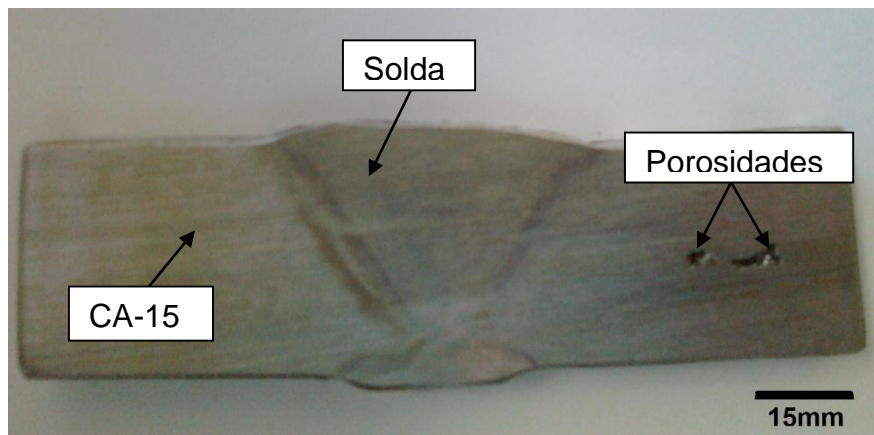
Imagem do Aço CA-15 após a soldagem e defeitos presentes no metal base.
